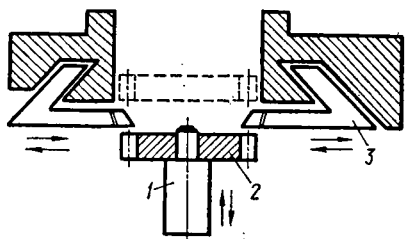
Схема нарезания зубьев цилиндрических колес многорезцовыми зубодолбежными головками:
